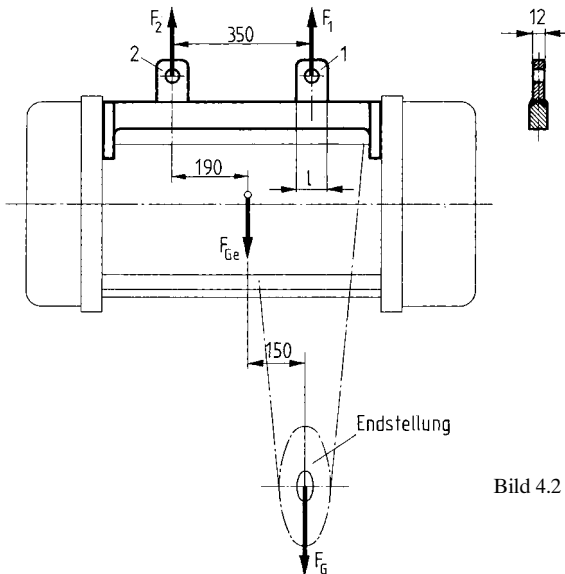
Geschweißte Ösen an einem Elektrosezug
